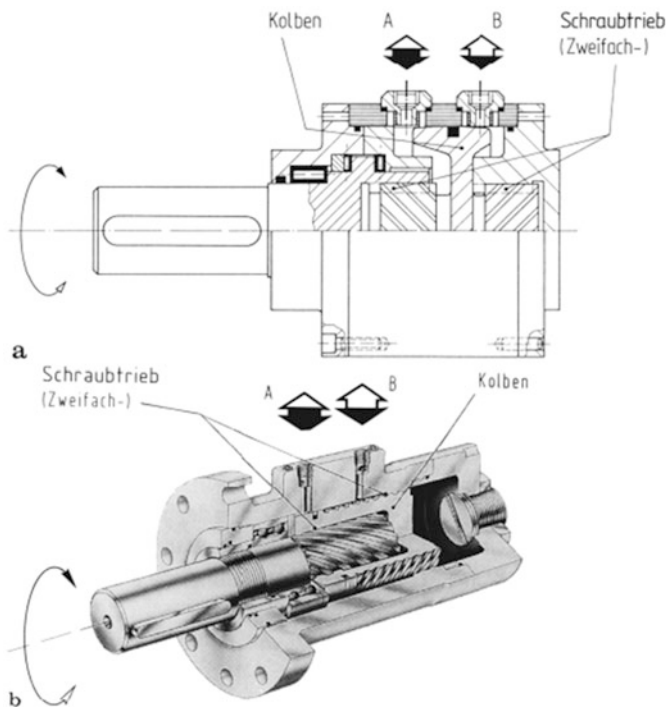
Steilgewindeschwenkmotor. a Serienkolbenmotor (ZD, Hausherr); b Parallelkolbenmotor (DZ, Hausherr)
